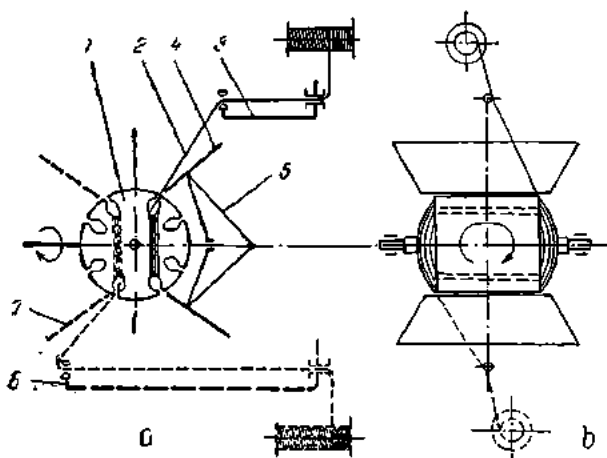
Schema cinematică a mașinii de bobinat automată pentru rotoarele motoarelor de mică putere, cu mișcare de rotație a rotorului ce se bobinează :
